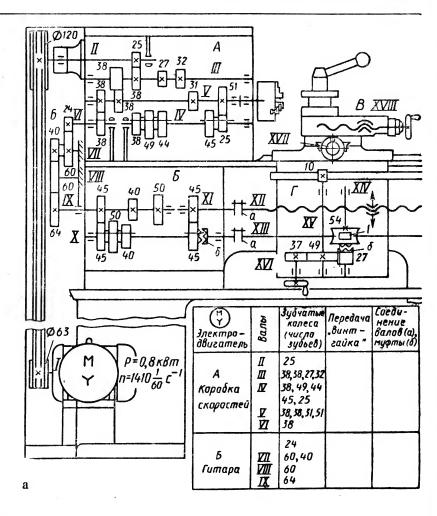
Механизмы токарно-винторезного станка ТВ-6.
